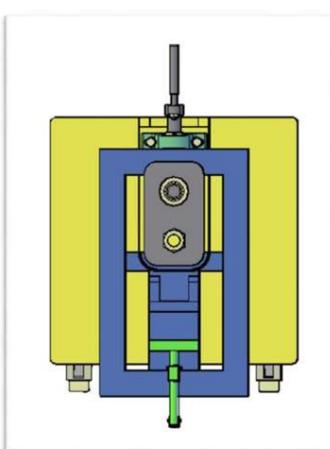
Tampak Depan Desain Meja Las Terpilih
